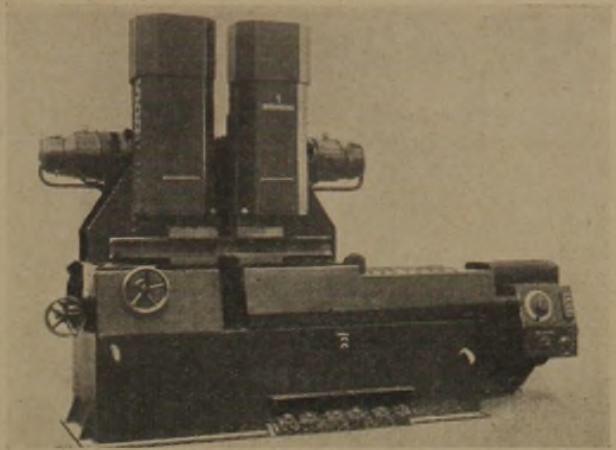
Selbsttätige elektrische Stumpfschweißmaschine für Querschnitte bis 20 000 mm²
